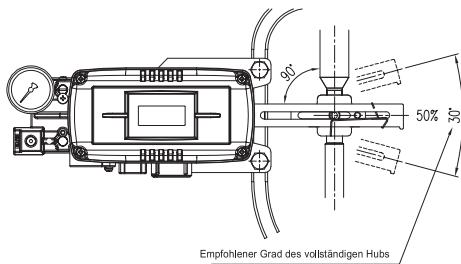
Linearer Rückführungshebel und Ventilschaft
